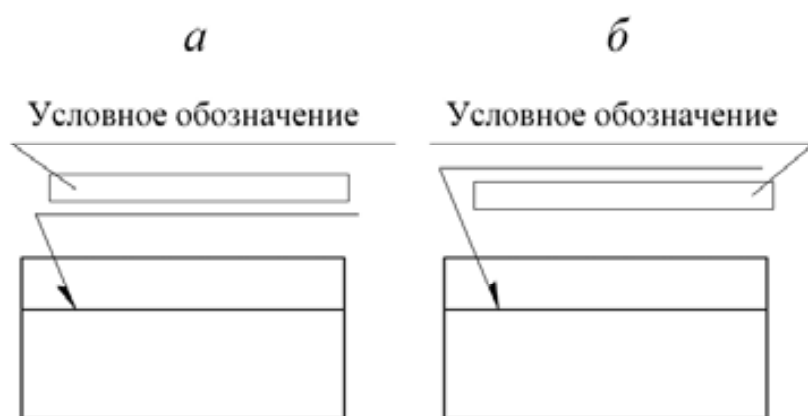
Условное обозначение сварного шва: *а* – с лицевой стороны; *б* – с оборотной стороны
